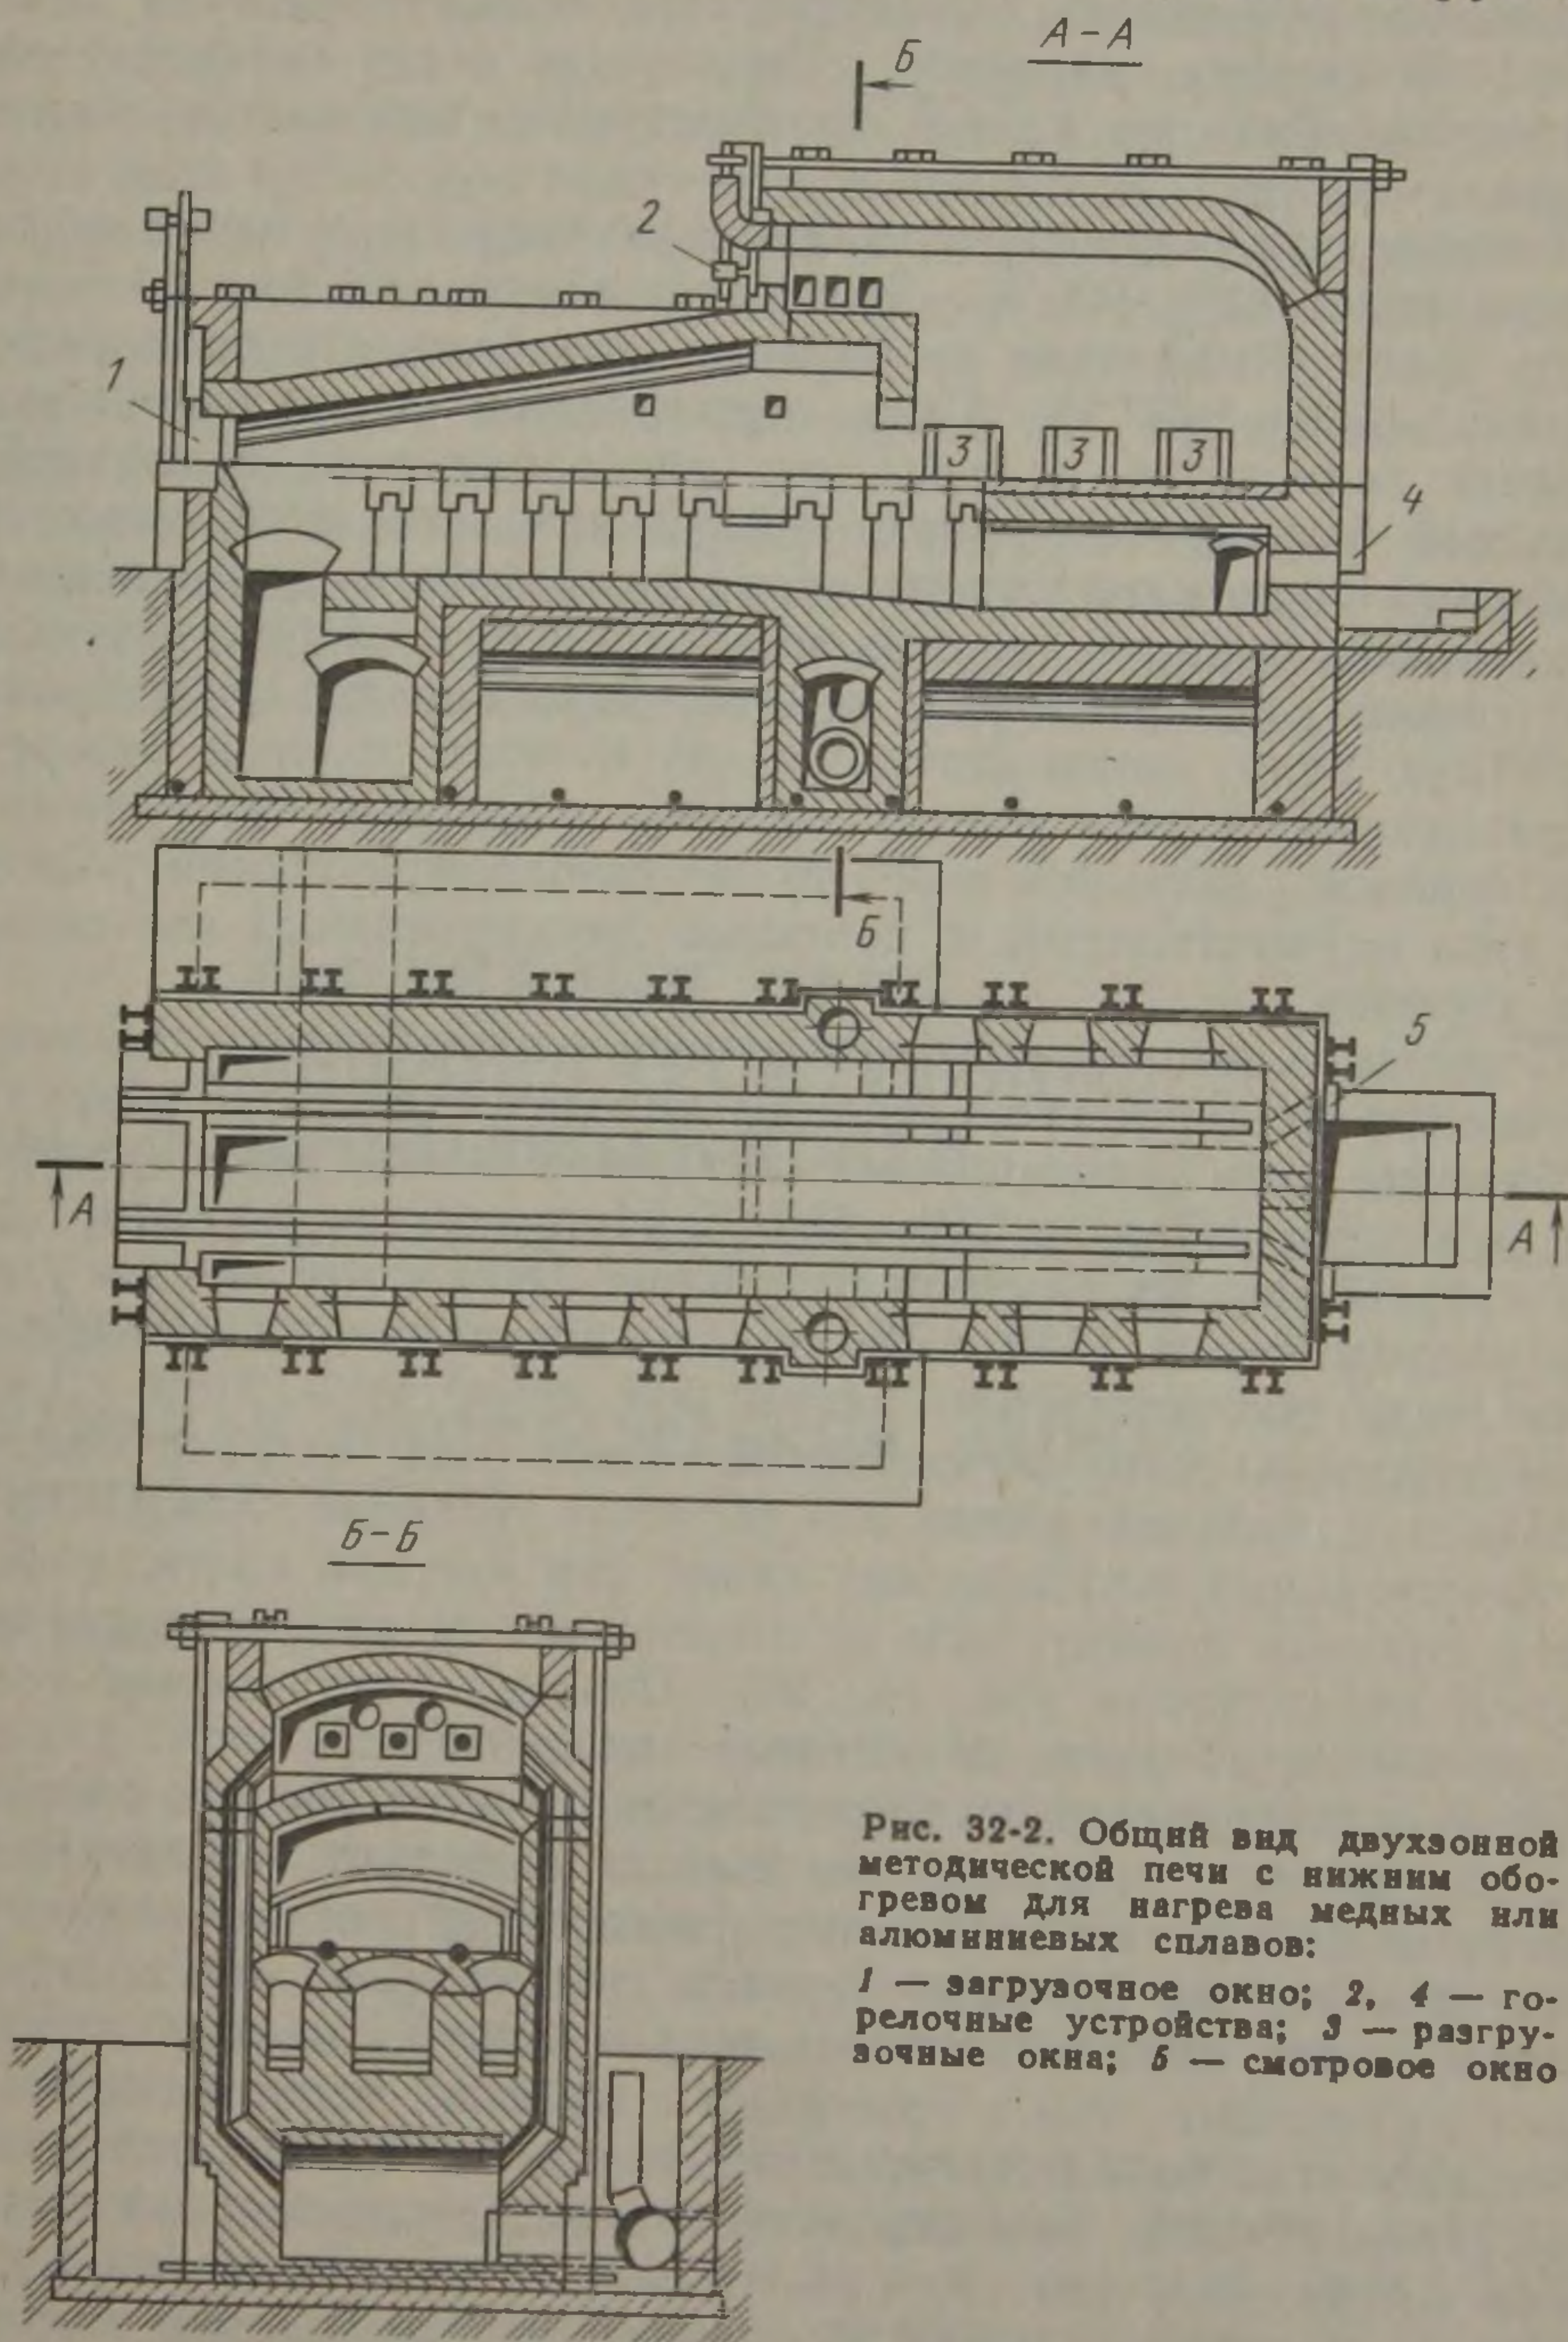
Общий вид двухзонной методической печи с нижним обогревом для нагрева медных или алюминиевых сплавов:
